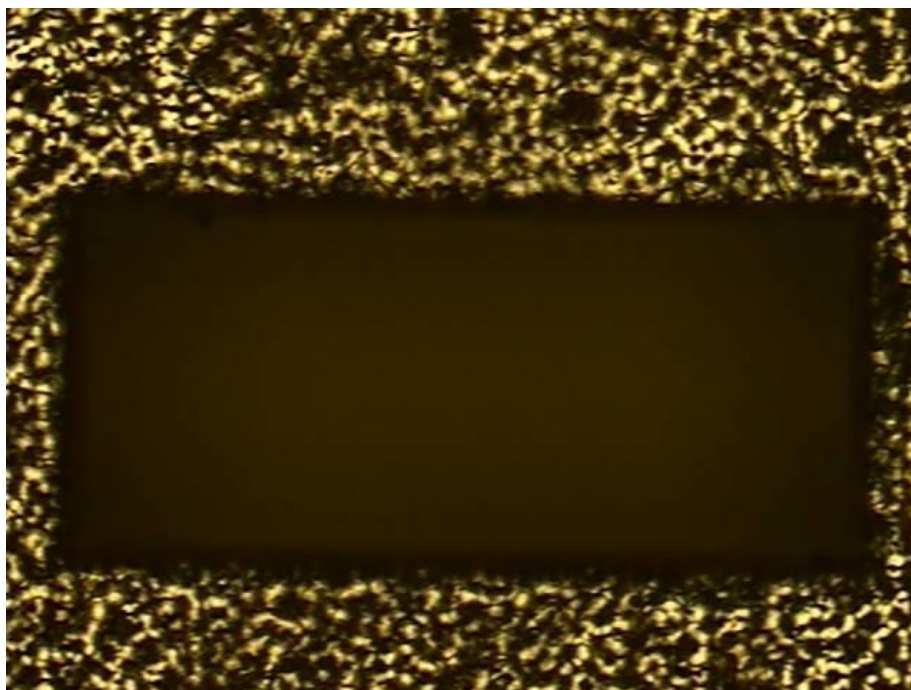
Detalle de un slot con 160 pasadas de excavado
